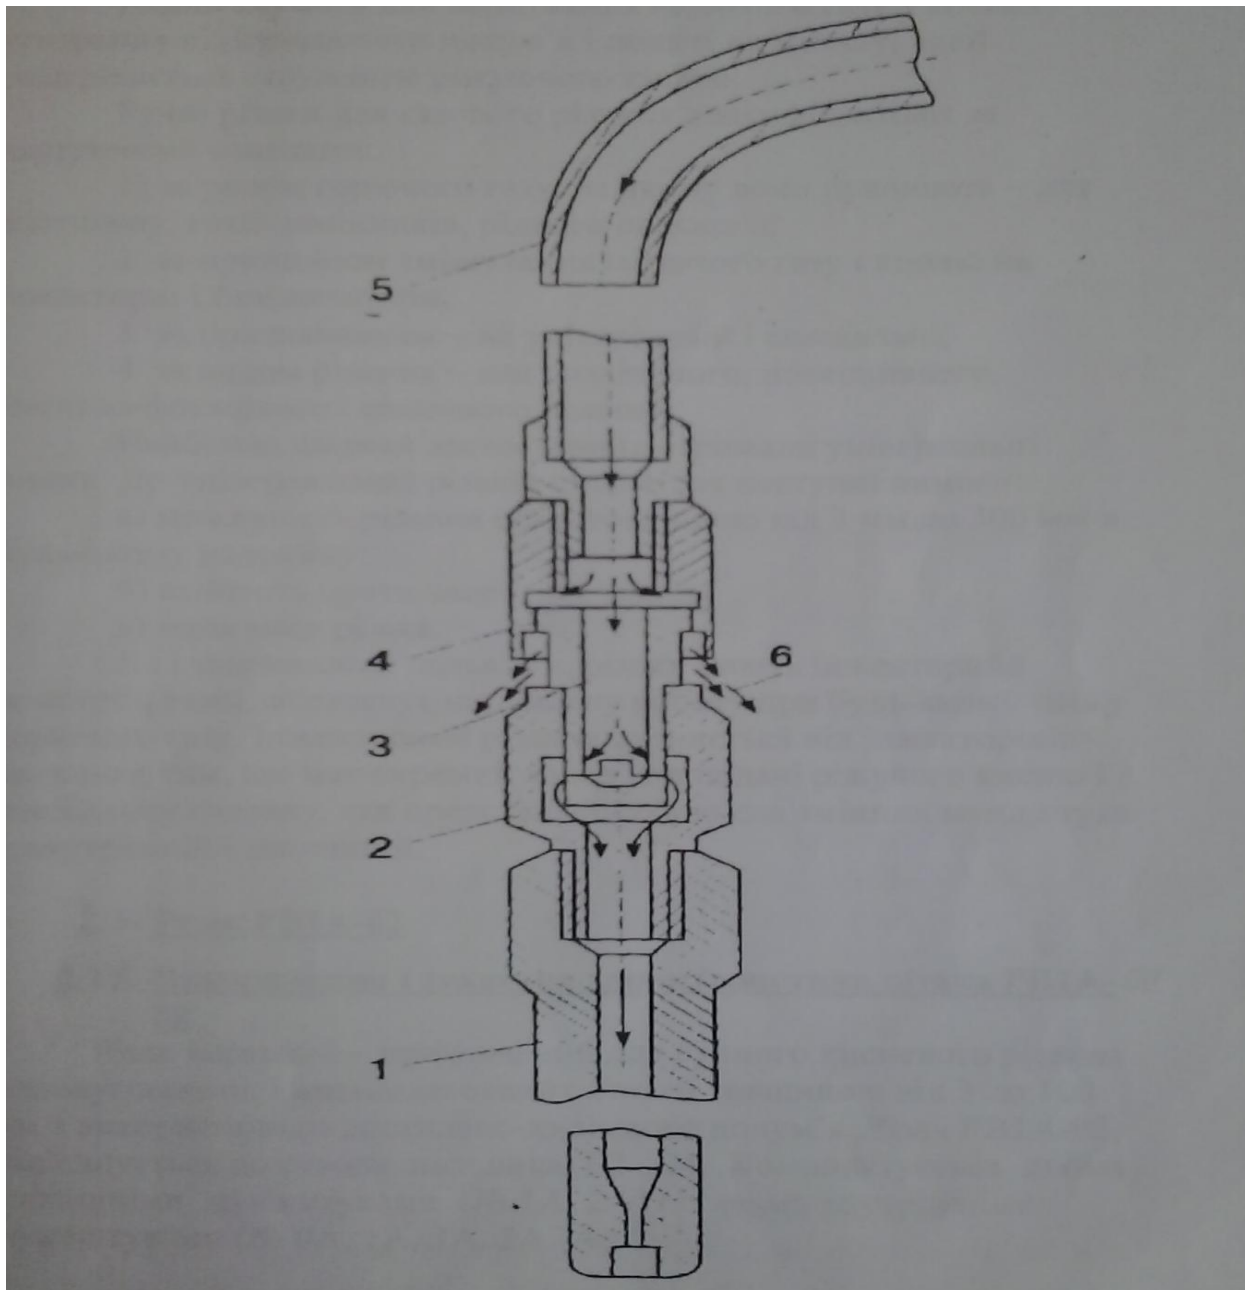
Конструкція мундштука пальника для зварювання газами заміниками ацетилену
